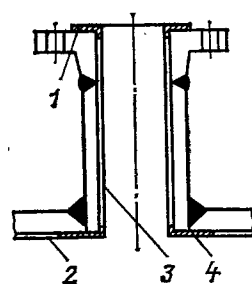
Патрубок с втулкой: 1 — наплавка сваркой; 2 — покрытие; 3 — втулка патрубка; 4 — наплавка сваркой
